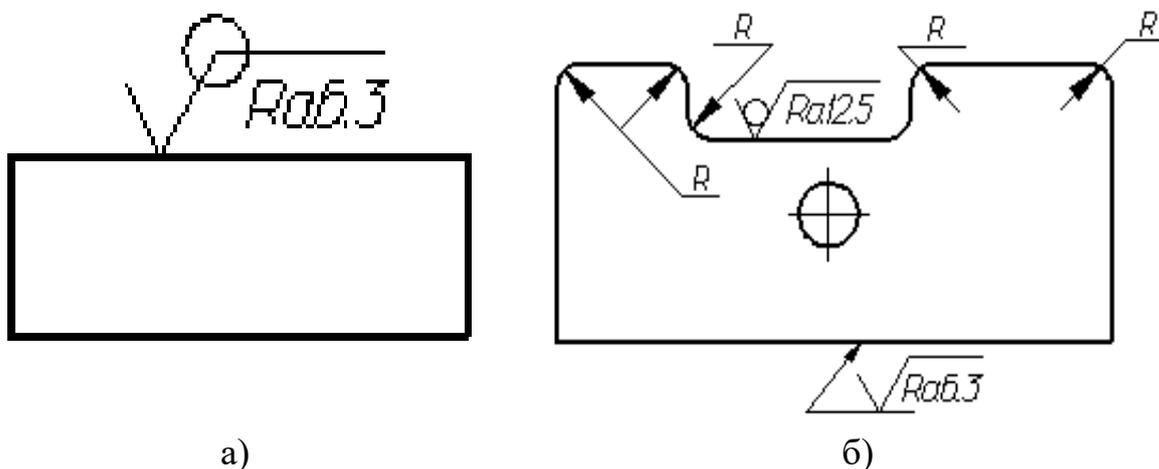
Обозначение поверхностей одинаковой шероховатости:
